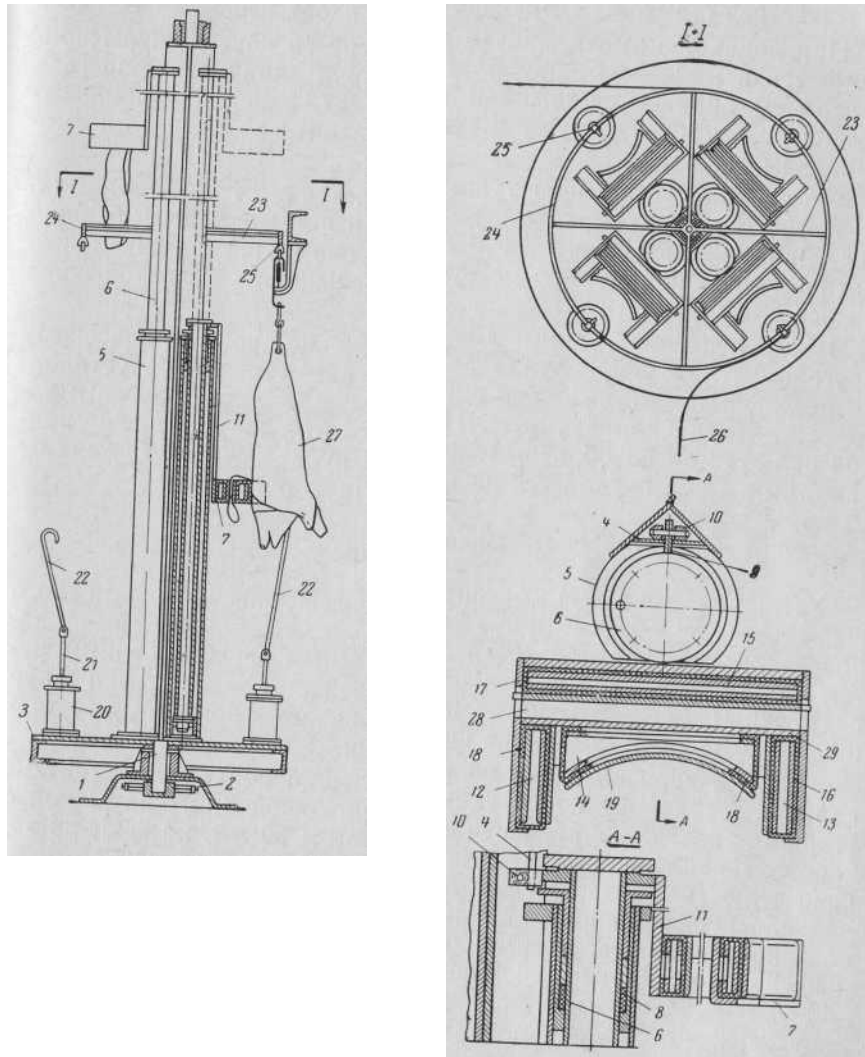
Установка з пневмоприводом для зняття шкур з туш свиней
